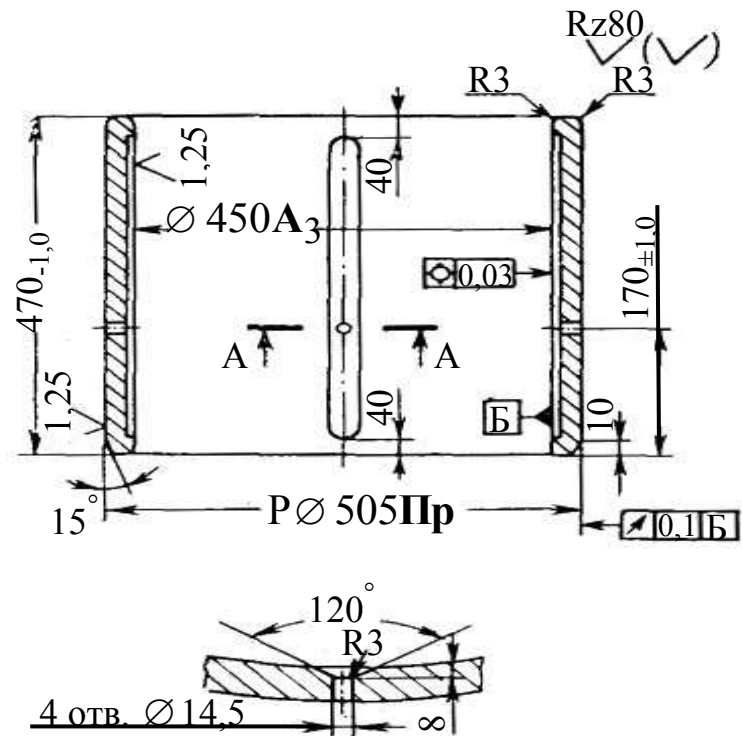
Ремонтный чертеж втулки центральной цапфы
